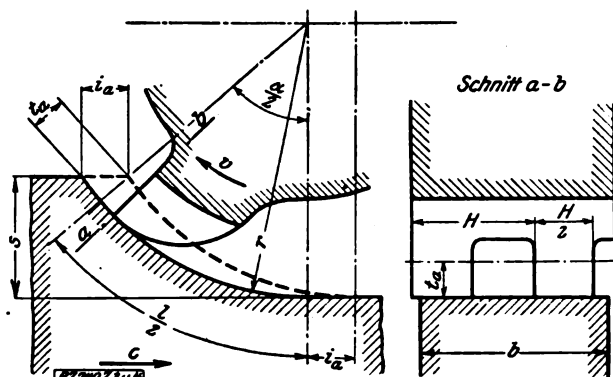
und 4. Schruppfräser mit Flachgewinde.
